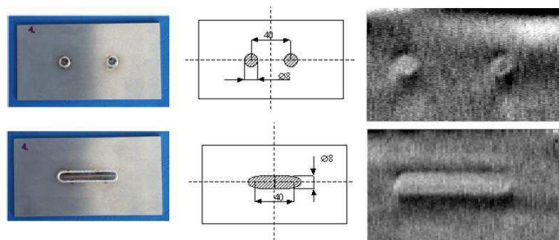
UDIMET-720[®]-Proben mit Waspaloy[®]-Auftragsschweißung. Links: Fotos der Proben nach der Auftragsschweißung. Die Proben wurden anschließend abgeschliffen, so dass die Aufträge visuell nicht mehr erkennbar waren. Mitte: technische Zeichnungen der Defekte. Rechts: im Scanverfahren aufgenommenes Magnetfeld in Schwarz-Weiß-Darstellung.
